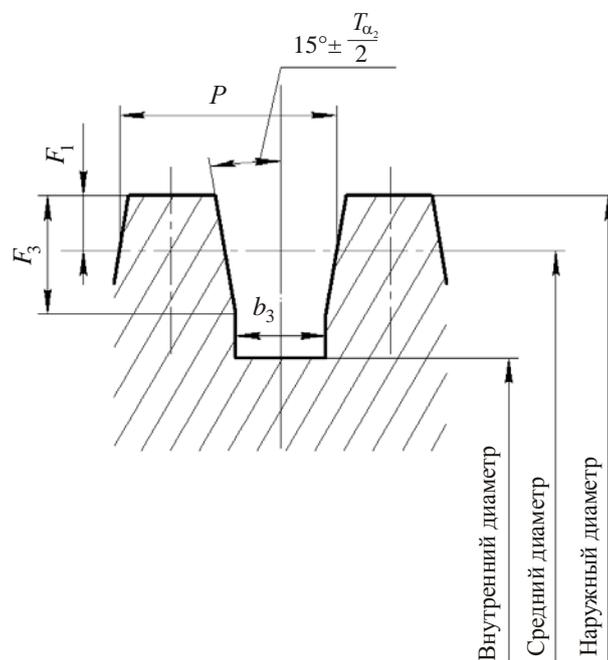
Укороченный профиль резьбы калибров-пробок для контроля внутренней трапецеидальной резьбы
